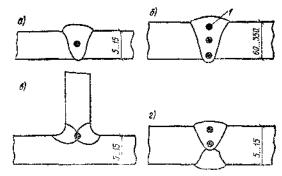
Схема вырезки образцов для непштания металла шва на растяжение при различной толицине основного металла, мм (q-r) — место вырезки образца
